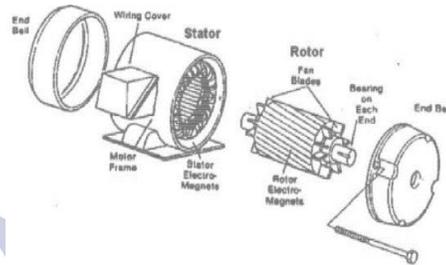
Gambar motor induksi 3 fasa tipe rotor sangkar tupai (*squirrel-cage rotor*).
